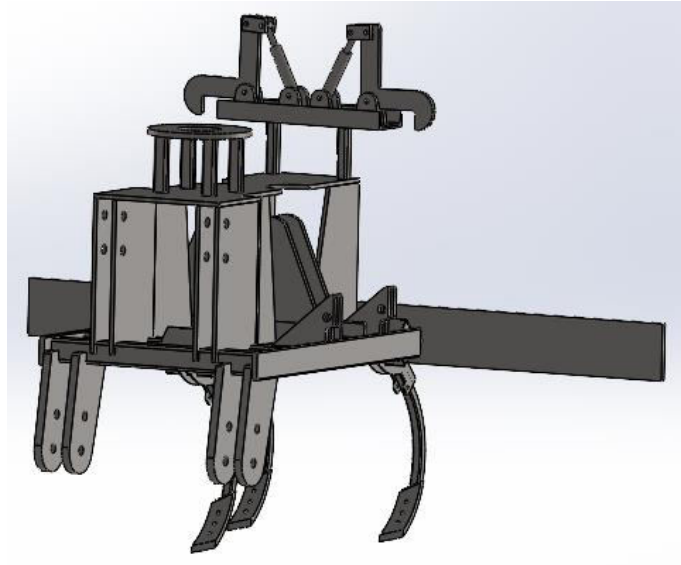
Alzado del ensamblaje final del bastidor fijo
